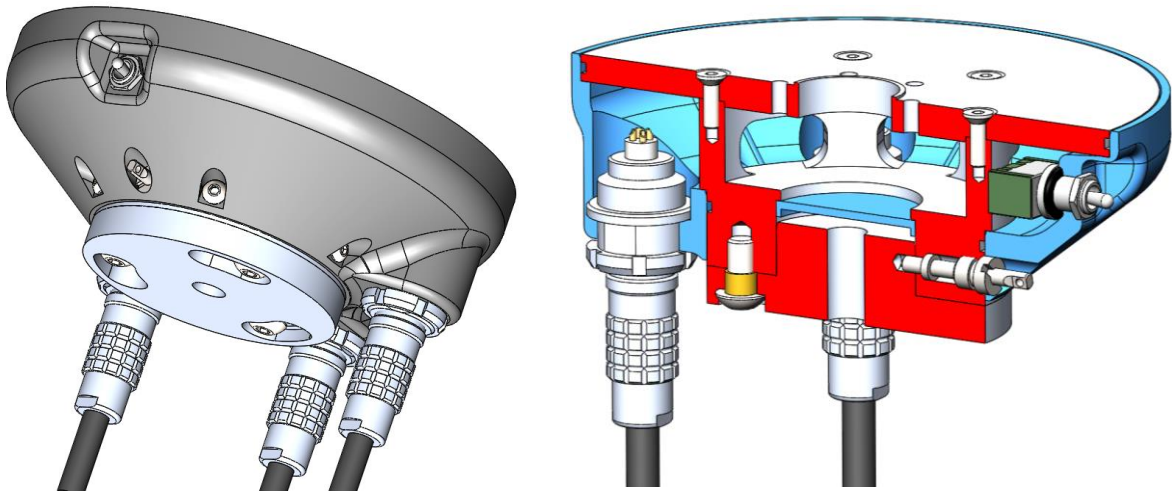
Base-Assembly (komplett): Gehäuse mit Buchsen und Schalter
